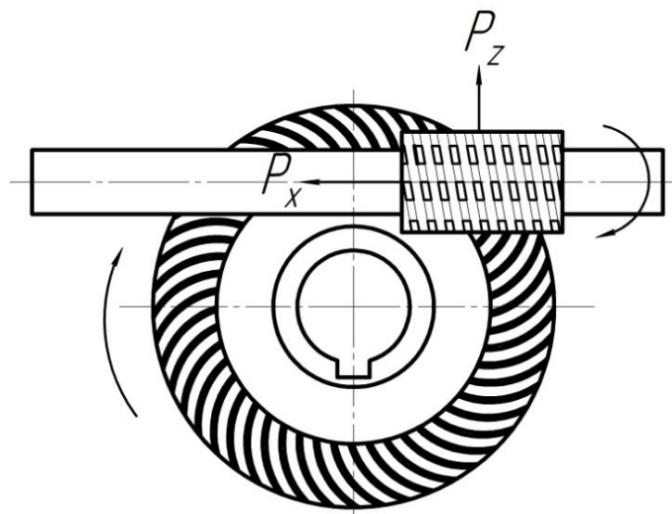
Расположение фрезы относительно нарезаемого колеса и изгиб оправки
